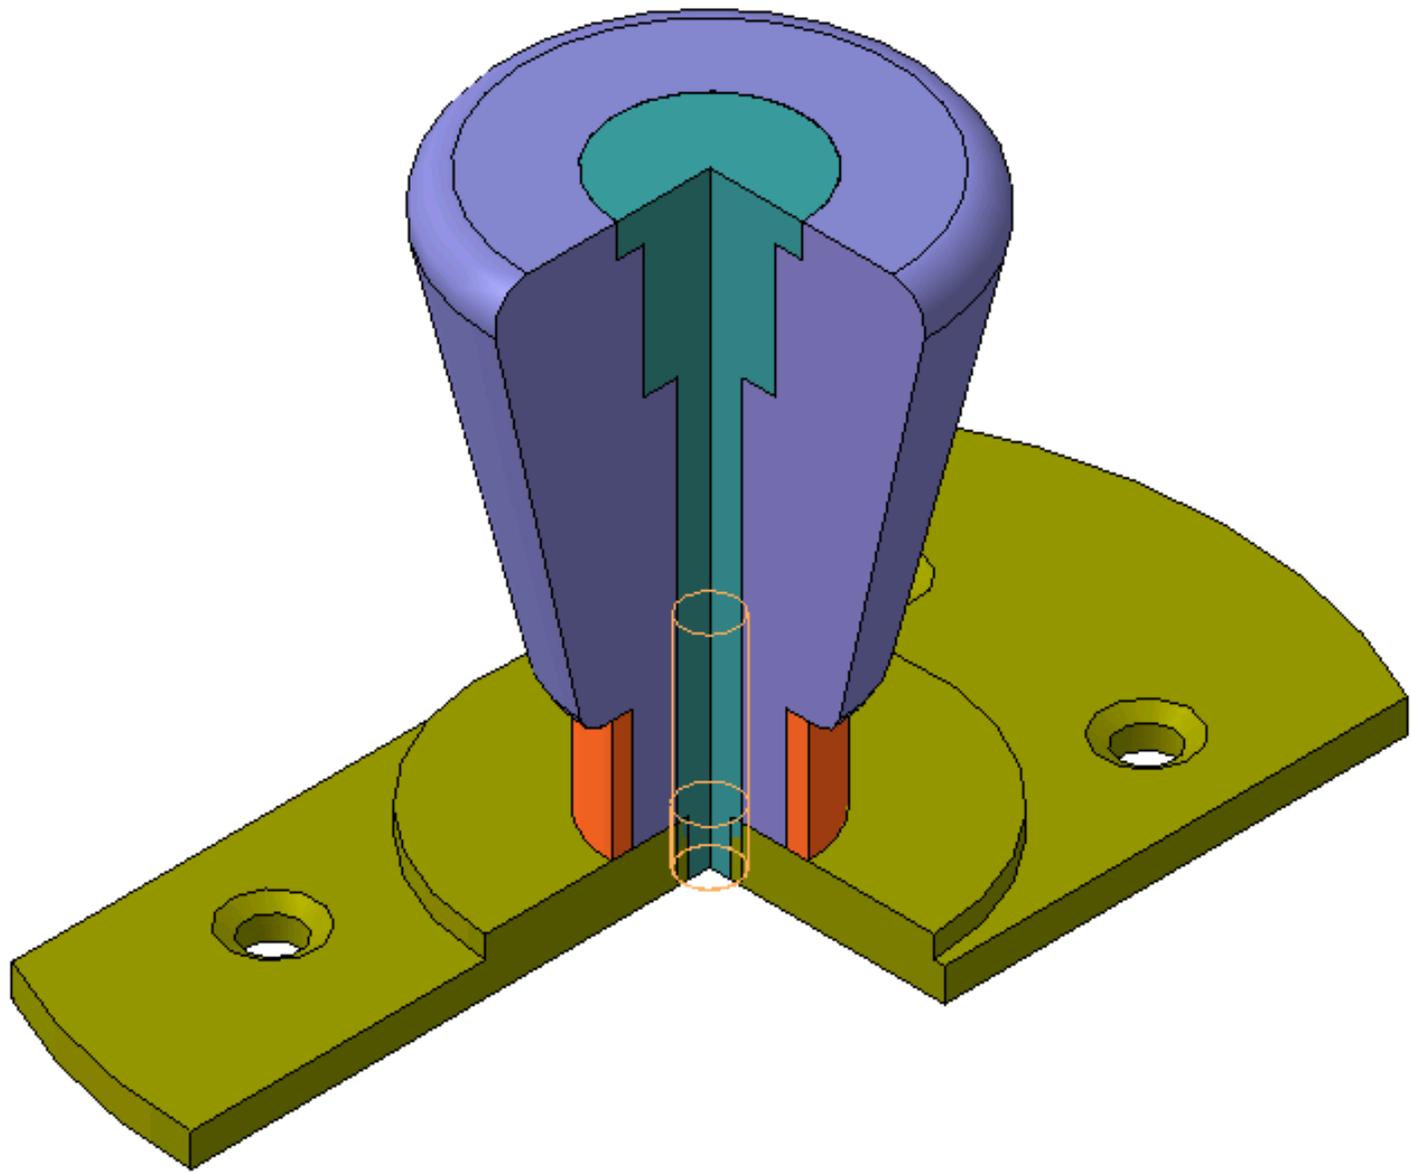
3D-модель сборки изделия «Ручка дверная» (варианты 7, 27)
